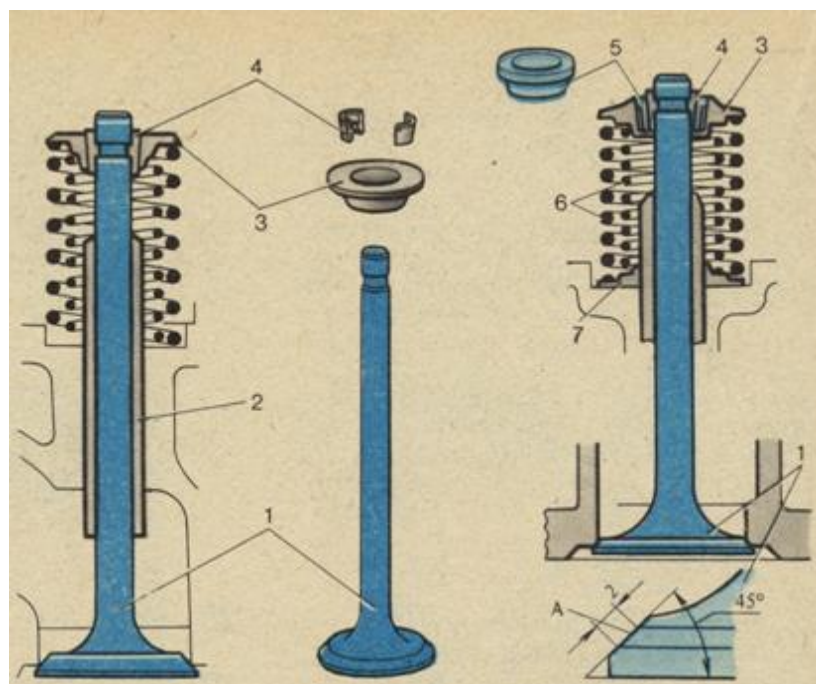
Клапанный механизм дизельных двигателей: 1 - клапан, 2 - направляющая втулка клапана, 3 - тарелка пружины, 4 - сухари, 5 - втулка сухарей, 6 - пружины, 7 - опорная шайба; фаска клапана
